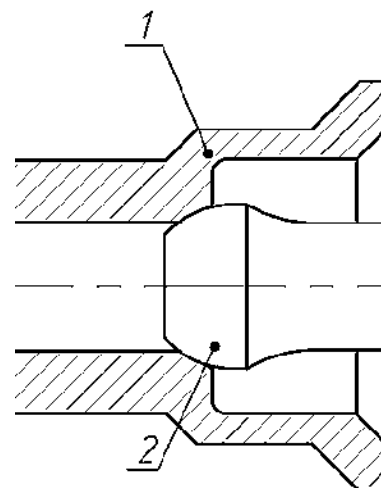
Посадка клапана по типу «конус-шар»: 1 – корпус; 2 – клапан
